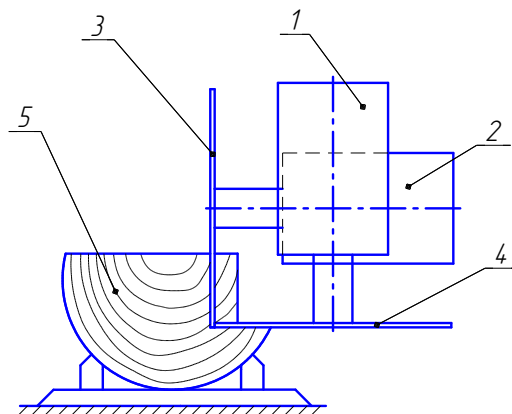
Принципова схема круглопилкового верстата для поздовжнього розпилювання колод із двома ортогонально розміщеними пилками:
